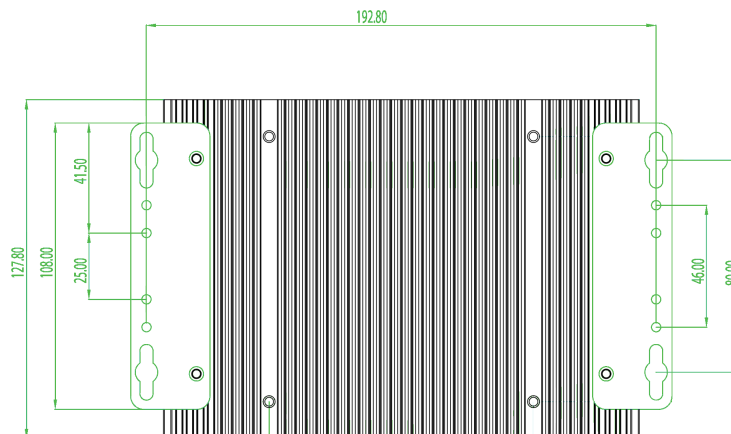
Encombrement (dimensions en mm) pour le montage en mural
